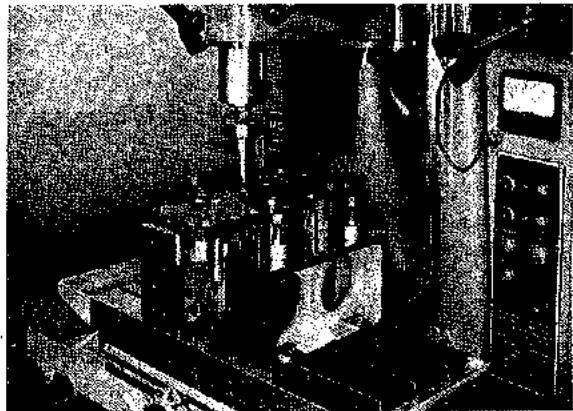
Mandrinado de los agujeros de una plantilla en una máquina para plantillas (Moore Special Tool Co., Inc.)
